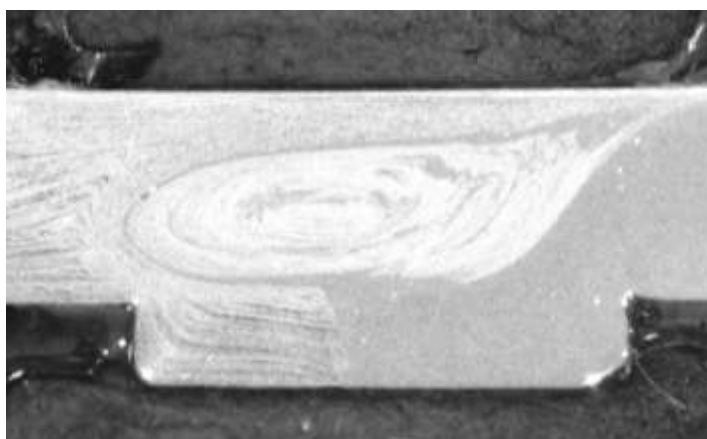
Структура сварного соединения сплавов В-1469 и АМг6
